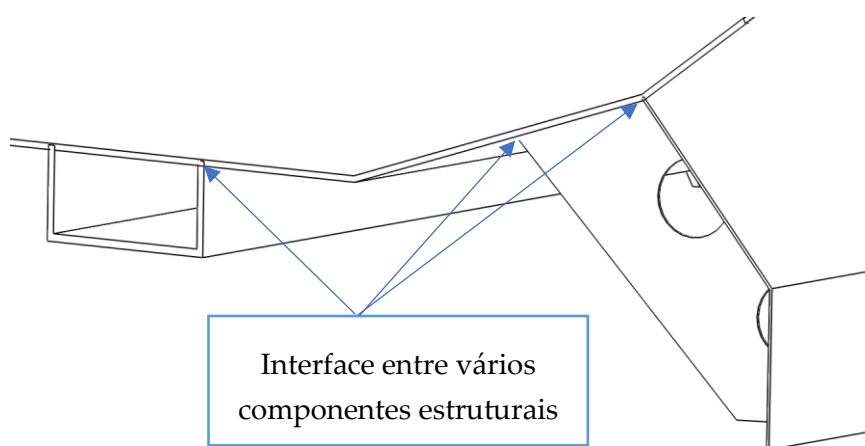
Interface entre vários componentes estruturais no *ASSEMBLY-SOLIDWORKS
